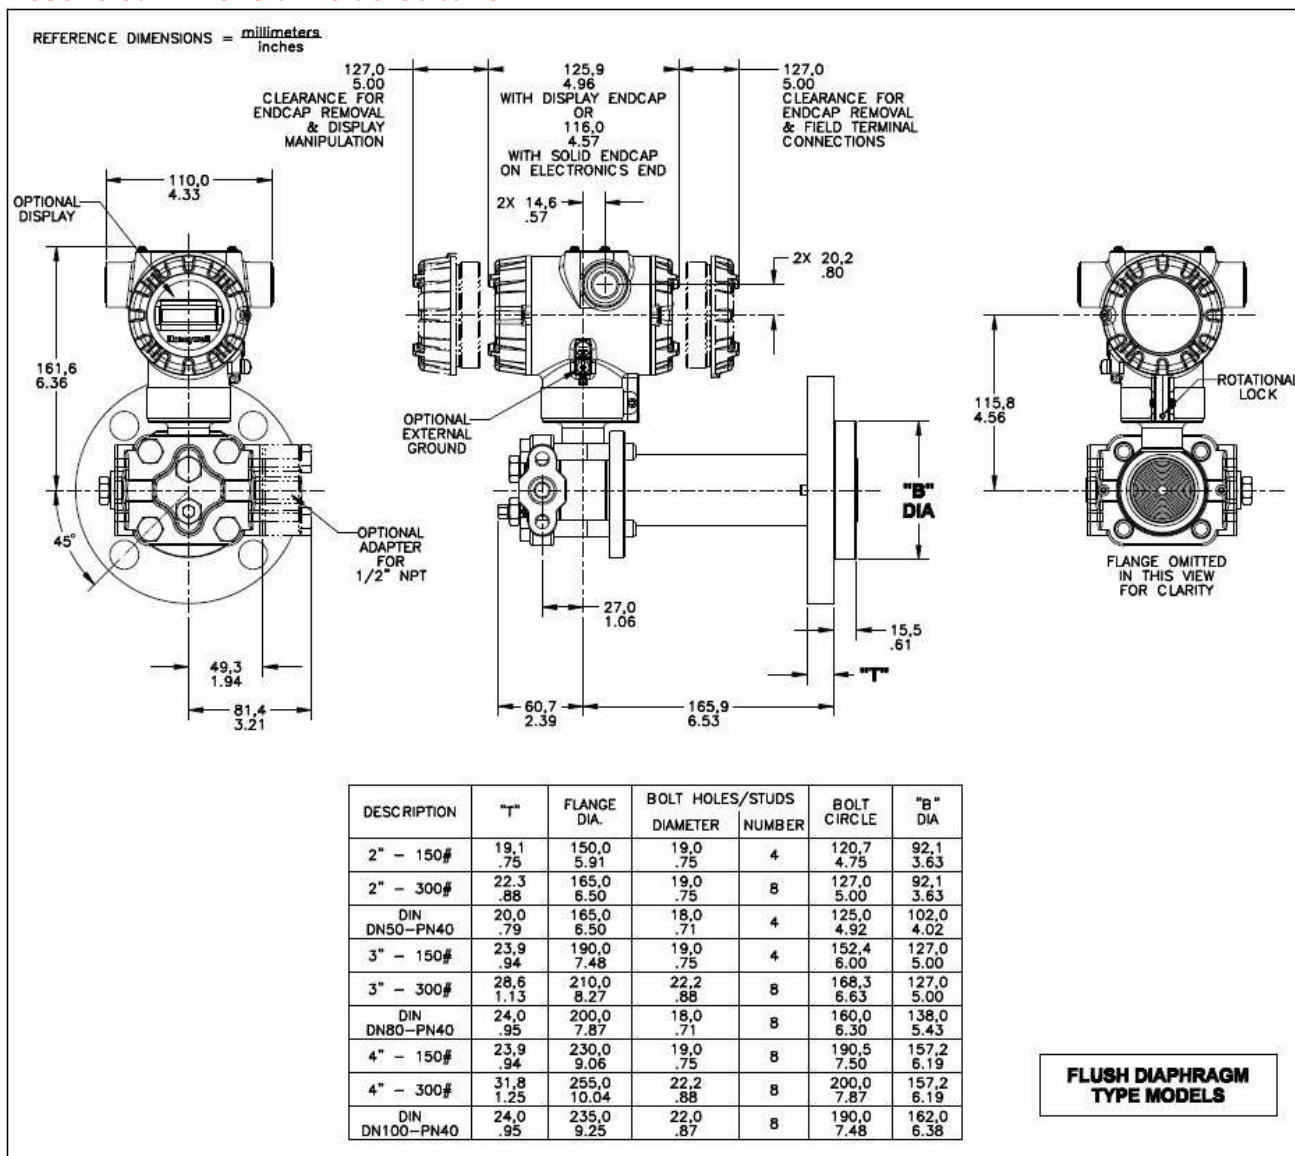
Dimensiuni de Montaj pentru Conectare Directa prin diafragma si flansa (fara extensie) la modele STF728 si STF732.
